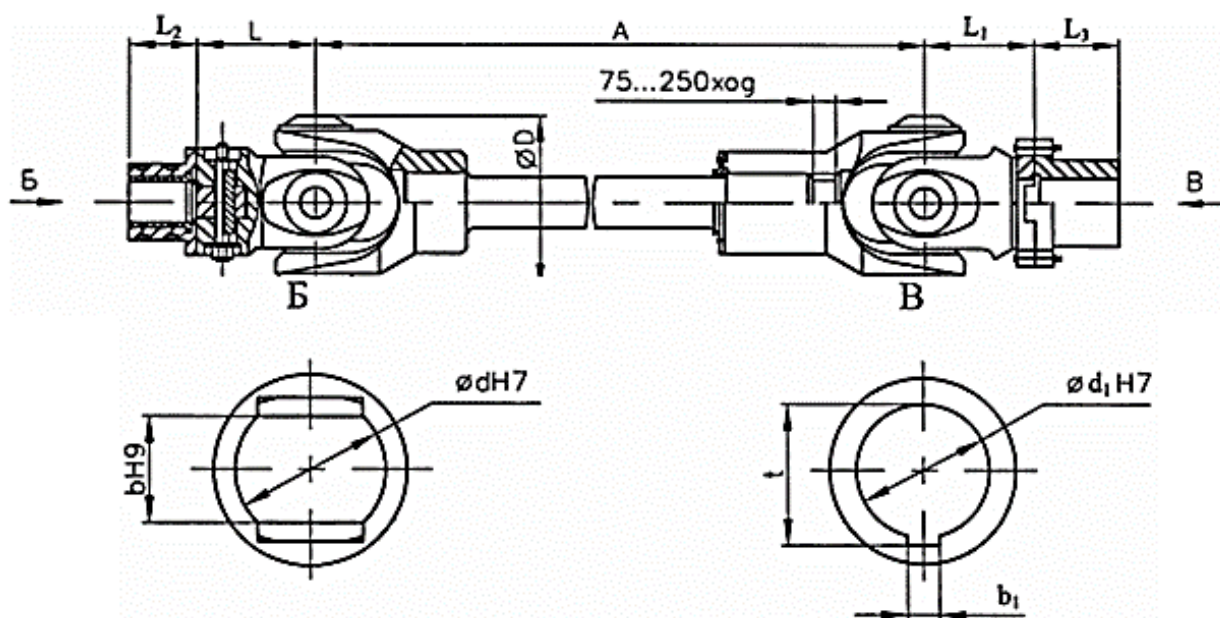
Универсальный шпиндель на подшипниках качения:
